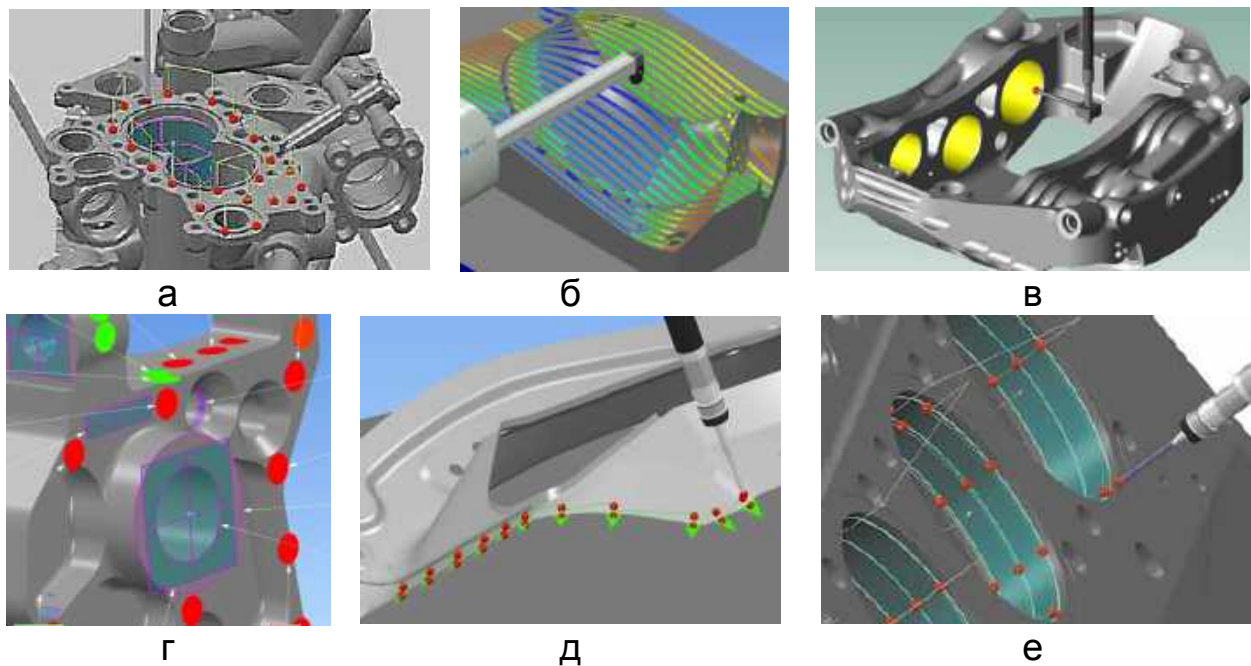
Комп'ютерна симуляція: а – точкового позиціонування; б – сканування; в – центрування; г – системи координат; д – вимірювання контуру на листовій деталі; е – контроль циліндричності отворів у корпусній деталі
